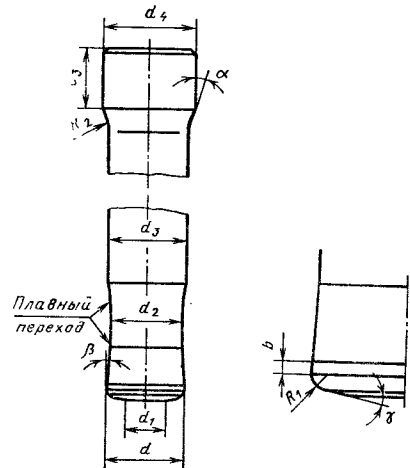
Твердосплавный пуансон для обратного выдавливания:
